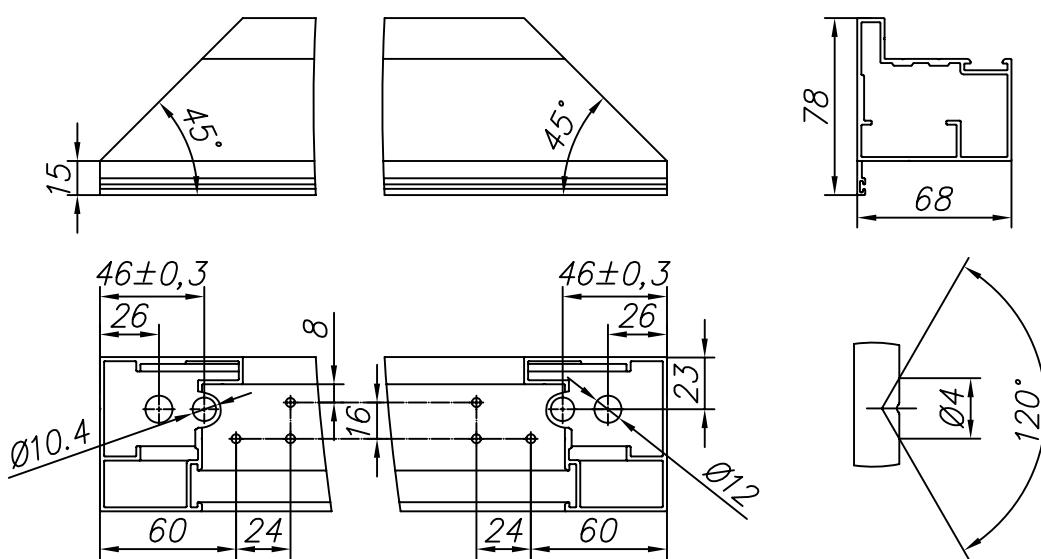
Изготовление стойки без паза для замка из профиля FLGU.400.0108 (открытие наружу)
